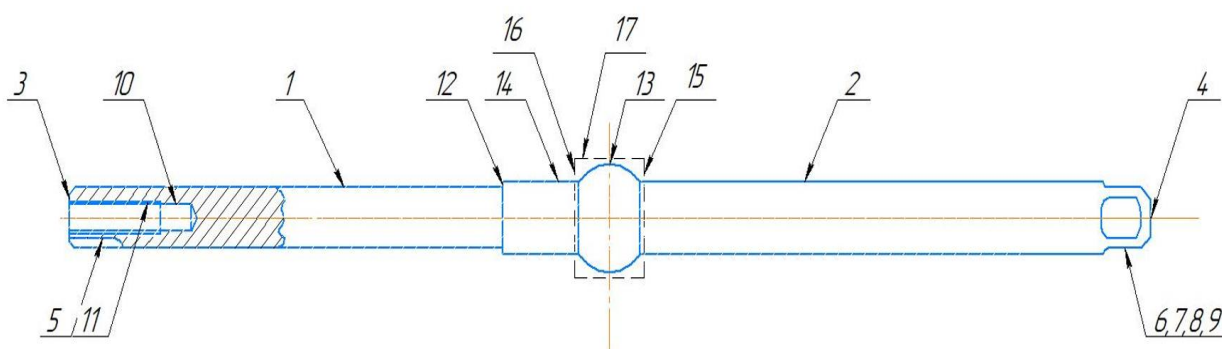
Эскиз детали с нумерацией поверхностей
